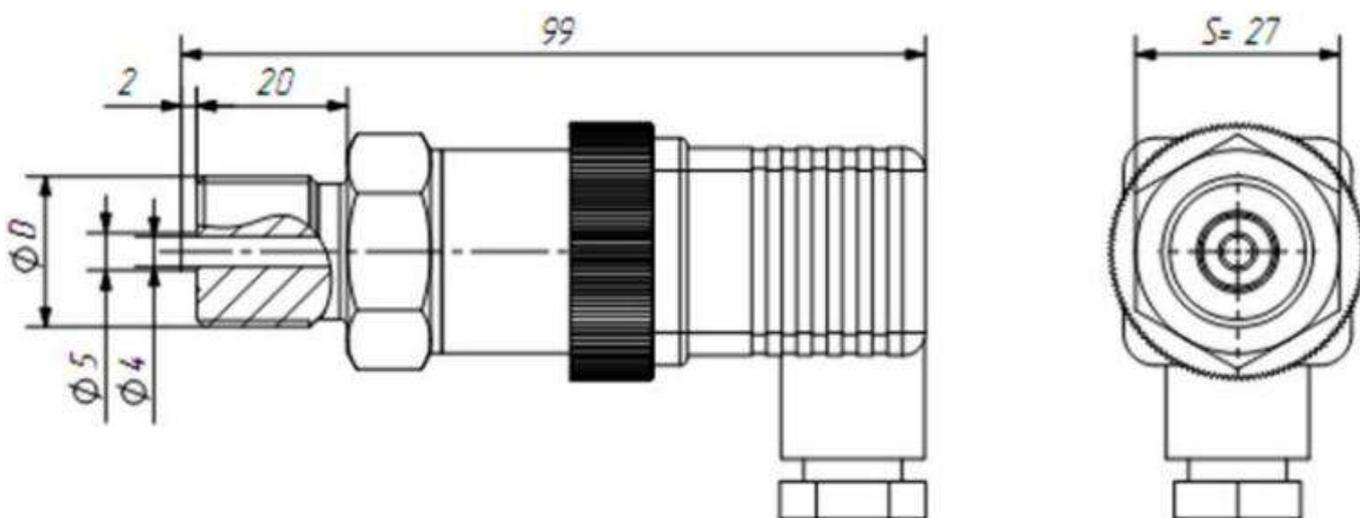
Габаритные и присоединительные размеры датчика ДДМТ-03Т-ДИ
